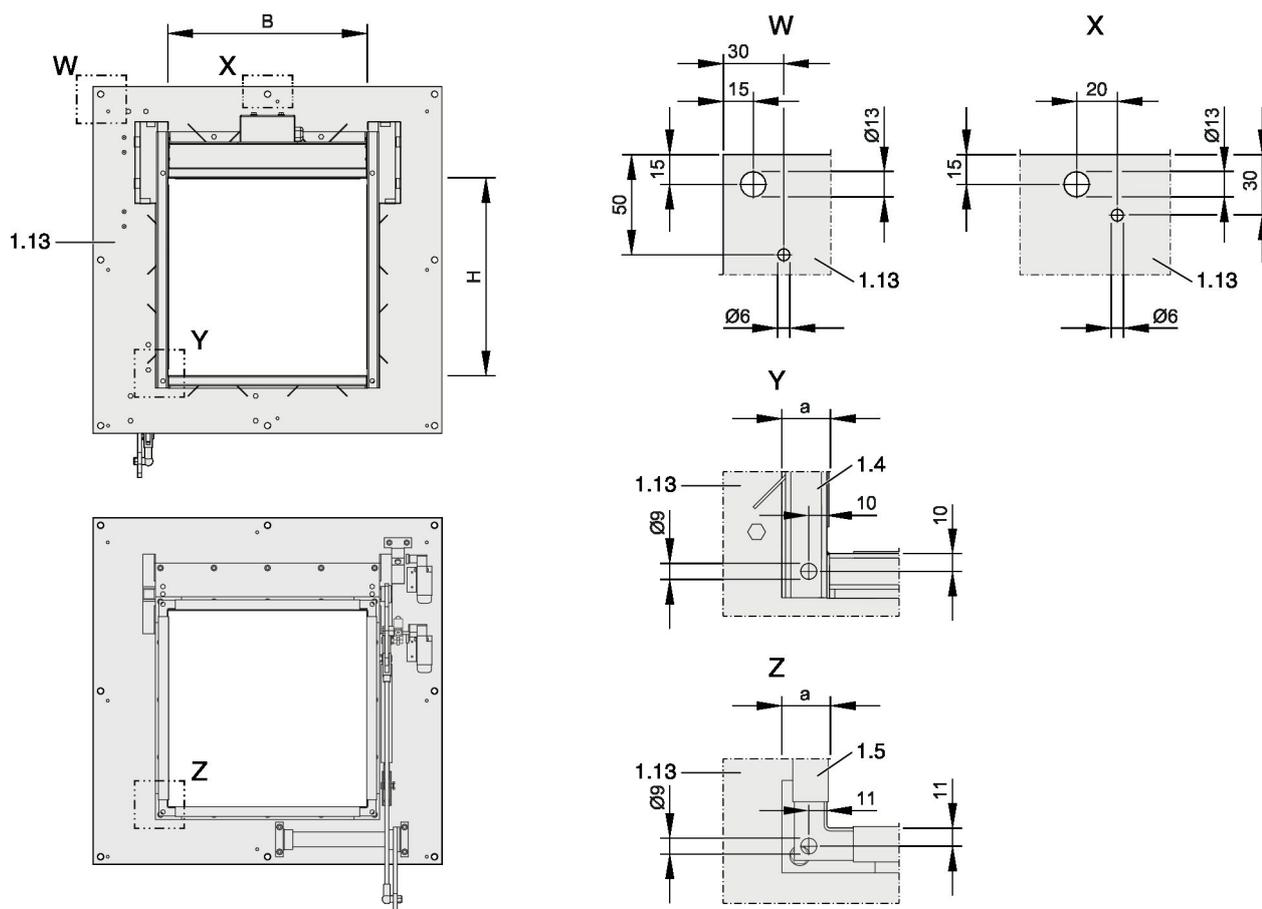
Bohrungen Montageplatte und Anschlussflansch
